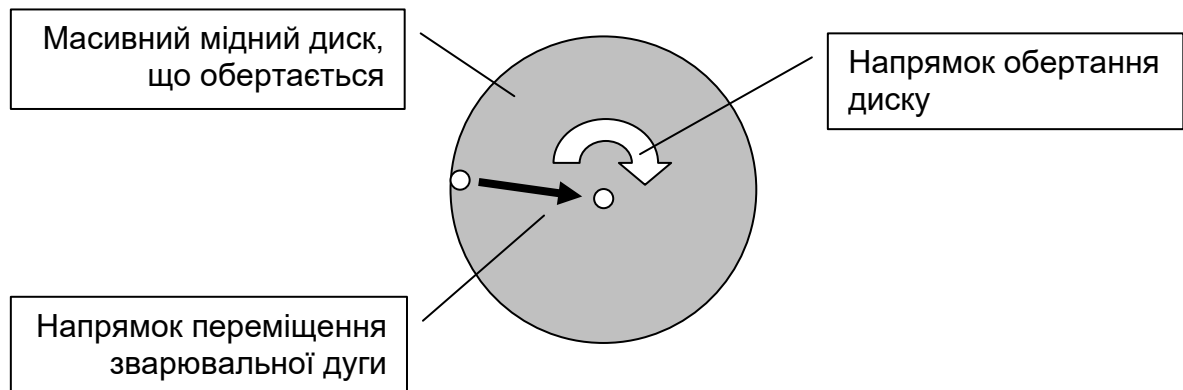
Схема наплавки на масивний мідний диск, що обертається
